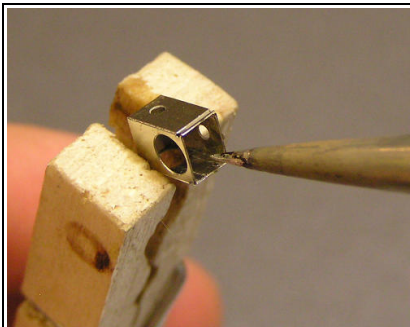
Getriebekasten in Holzklammer einspannen und alle 4 Innenkanten mit wenig Zinn verlöten.
